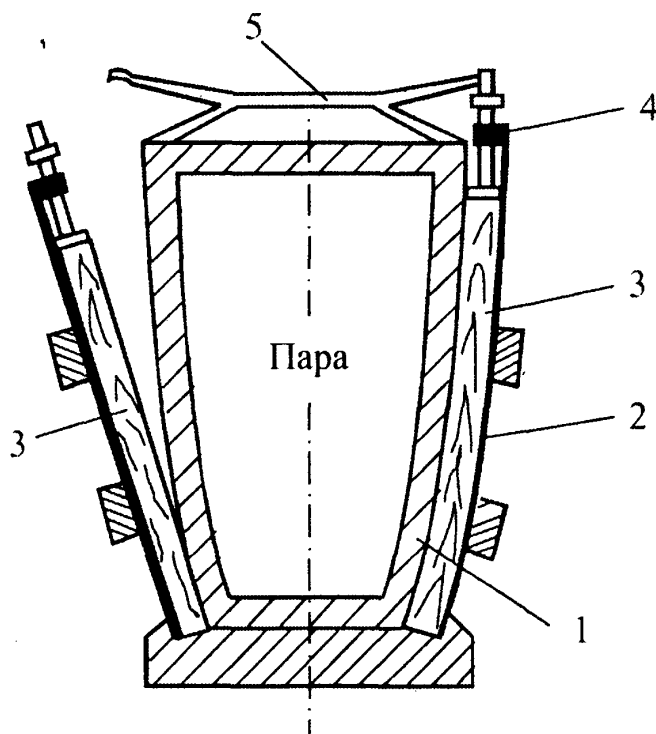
Схема гнударно-сушильного верстата: 1 - шаблон; 2 - шина; 3 - заготовка; 4 - торцеві упори шин; 5 - захват для утримання зігнутої заготовки
